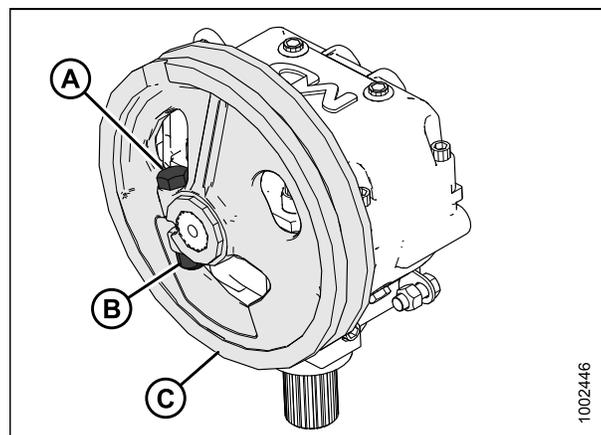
Редуктор привода ножа (МКШ) и шкив
